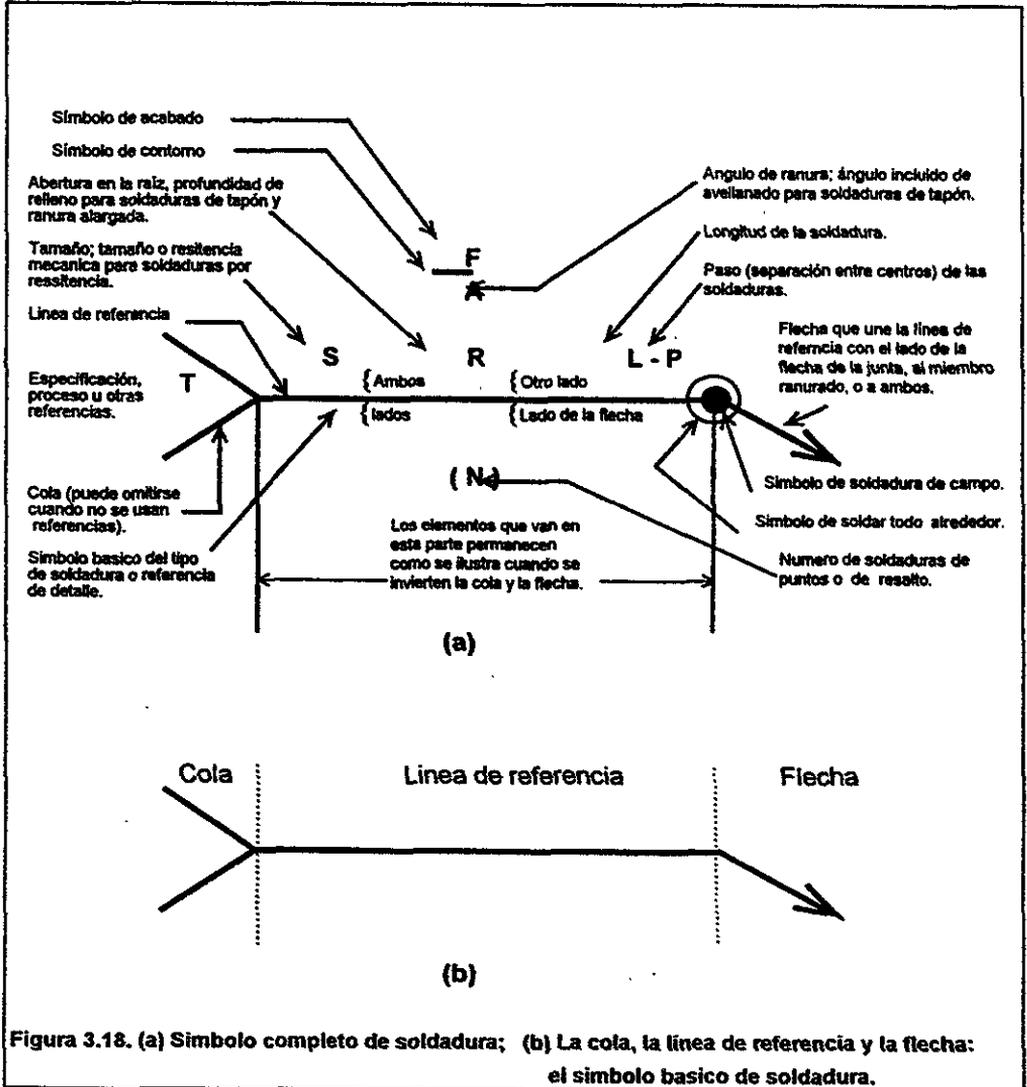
(a) Símbolo completo de soldadura; (b) La cola, la línea de referencia y la flecha: el símbolo básico de soldadura.
